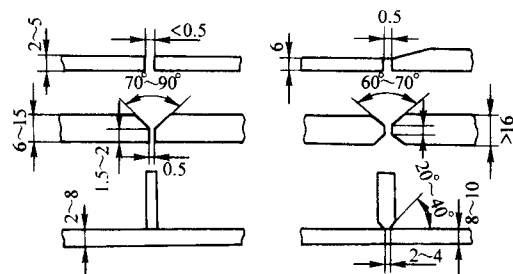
镁合金熔化极氩弧焊坡口形式
